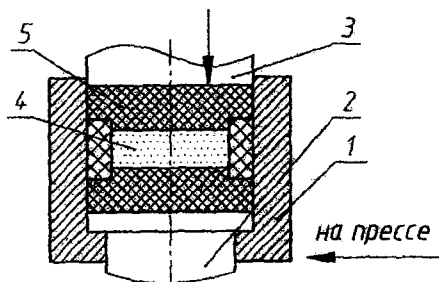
Квазистатическое прессование: 1 – оболочка; 2 – выталкиватель пресса; 3 – плунжер с приводом от ползуна пресса; 4 – порошок; 5 – элементы, из которых собирается резиновая оболочка
